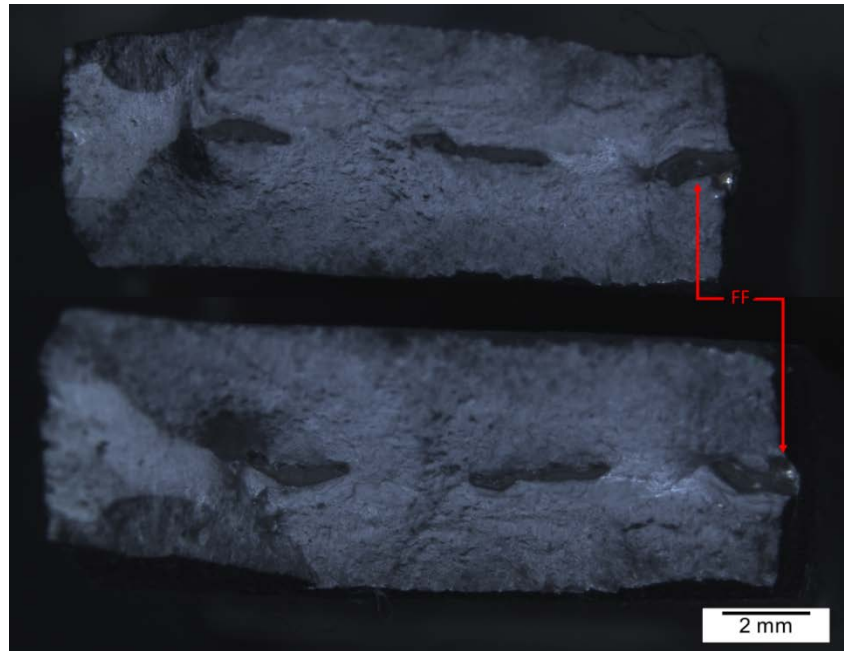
Imagen por estereoscopio de la fractura del ensayo de tensión T1 unión soldada ER312.
